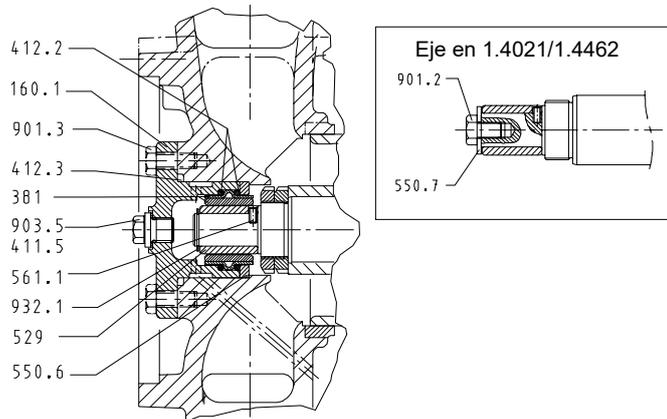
Desmontaje del cojinete liso: tubuladura de aspiración radial
